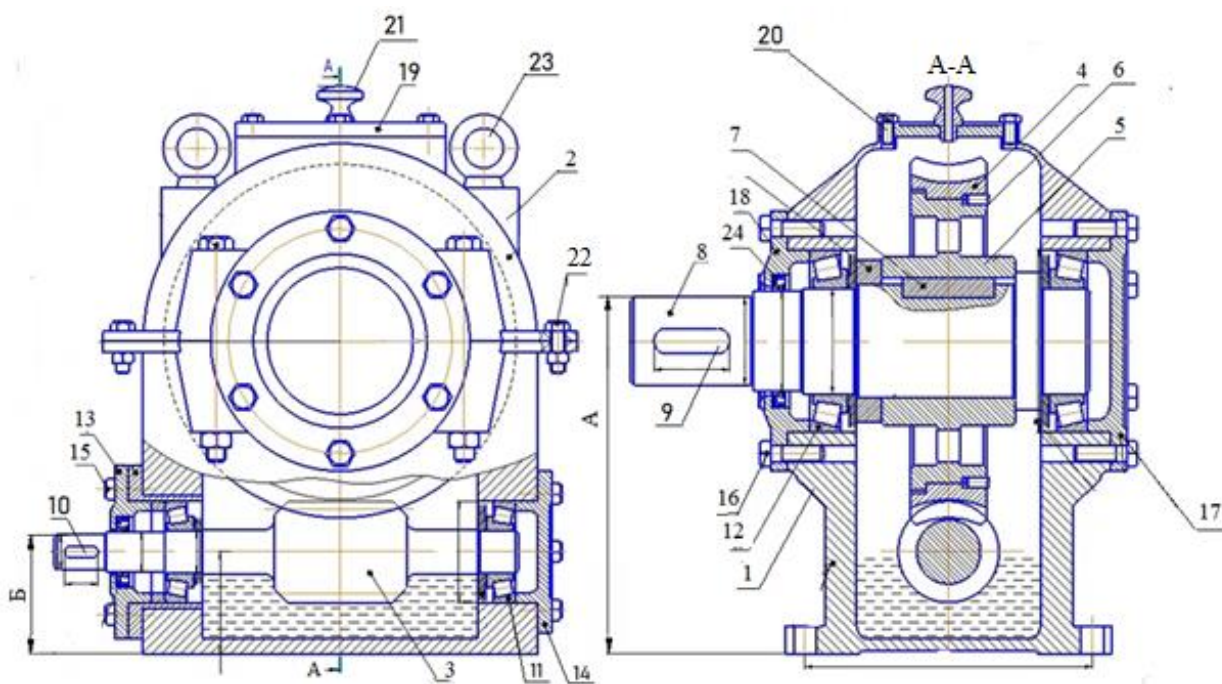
Червячный цилиндрический редуктор с нижним расположением червяка
